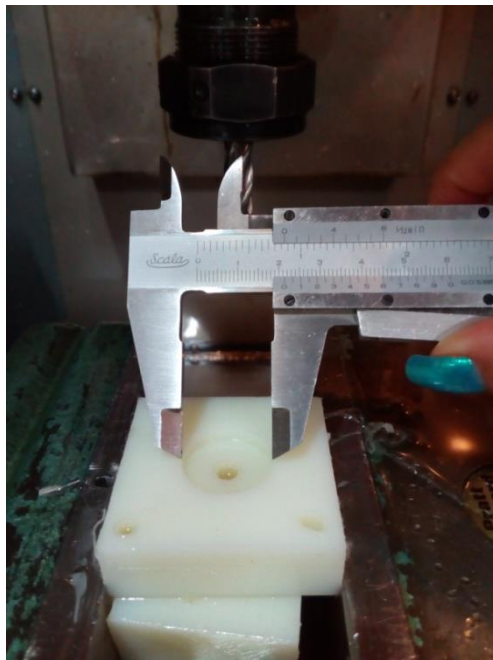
Fresado de la pieza Placa con un cortador de 1/2 in.
